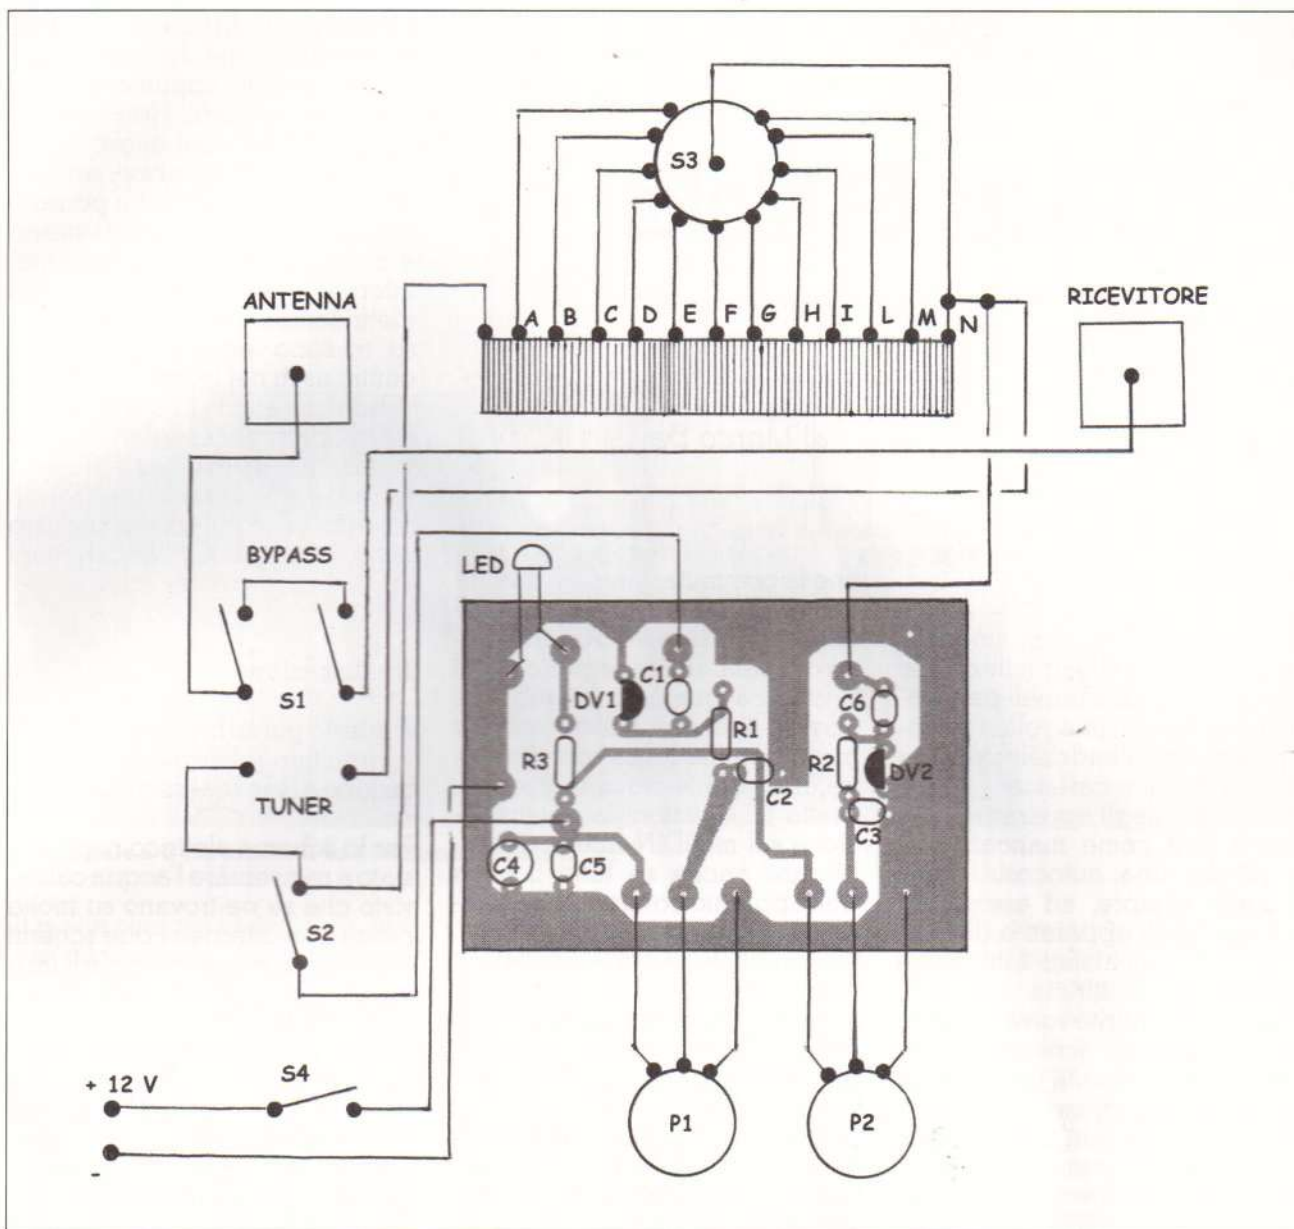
Accordatore a diodi Varicap per BCL e SWL (layout componenti)
